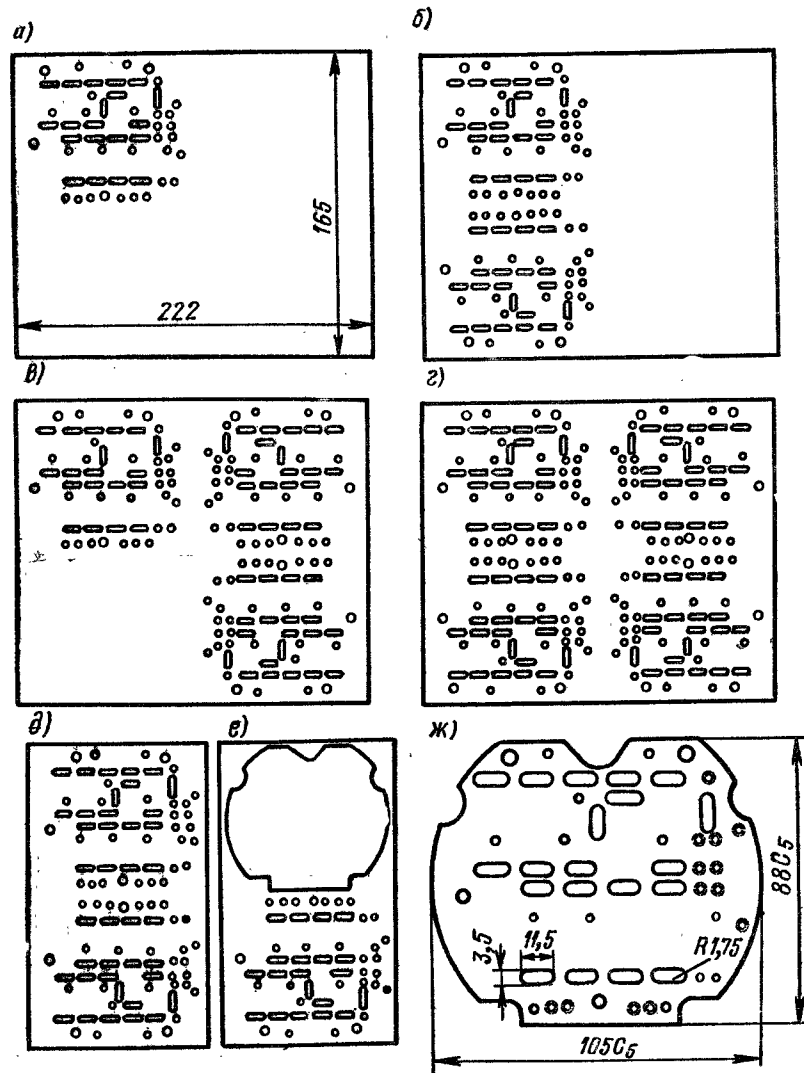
Последовательность штамповки отверстий в заготовке для четырех деталей
